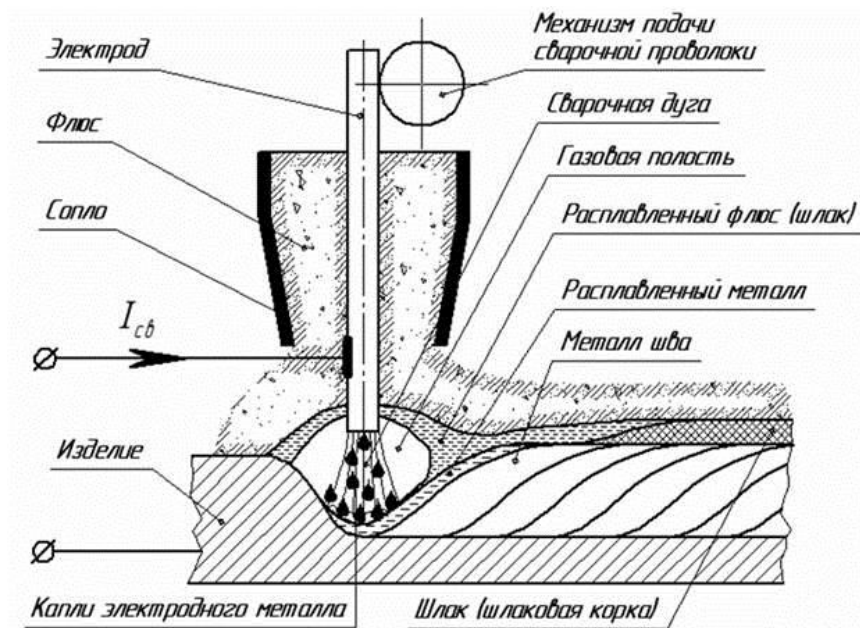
Схема автоматической сварки под слоем флюса
